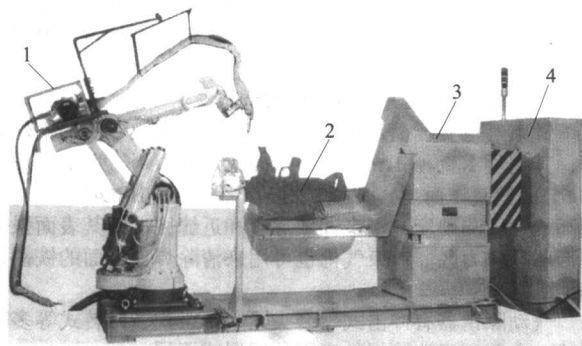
弧焊机器人与 L 型焊接变位机
